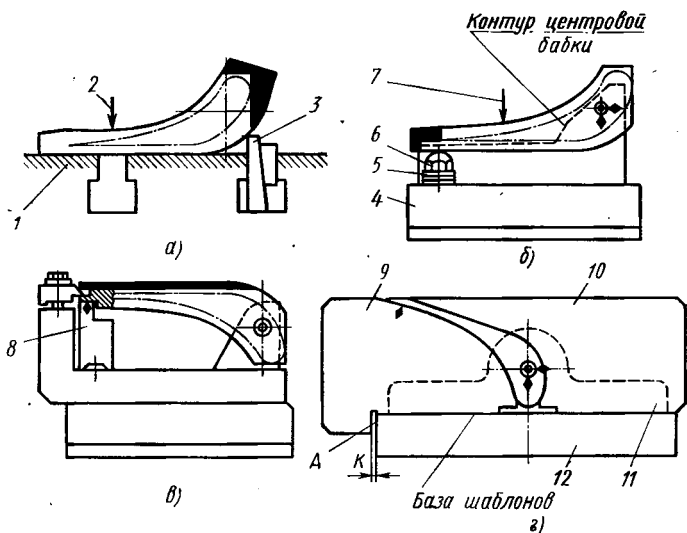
Схема обработки ковальной заготовки лопатки сложнопространственной формы:
